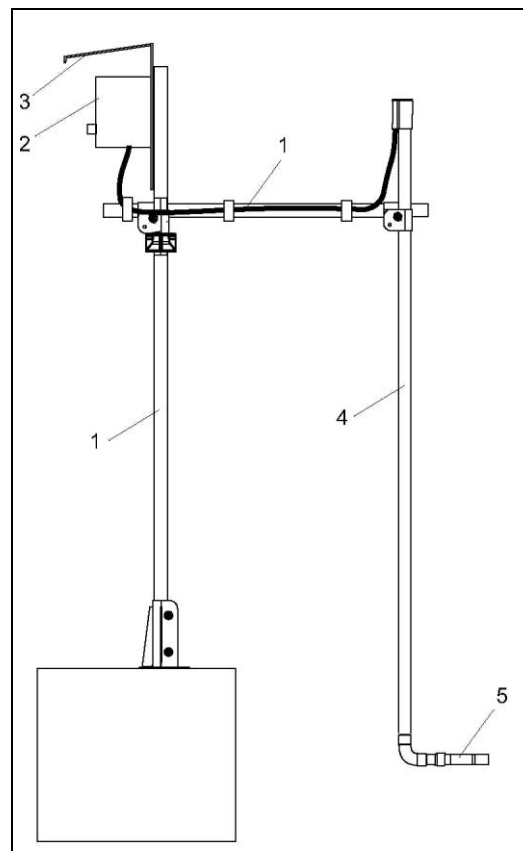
Монтаж под углом 90° на вертикальной стойке
